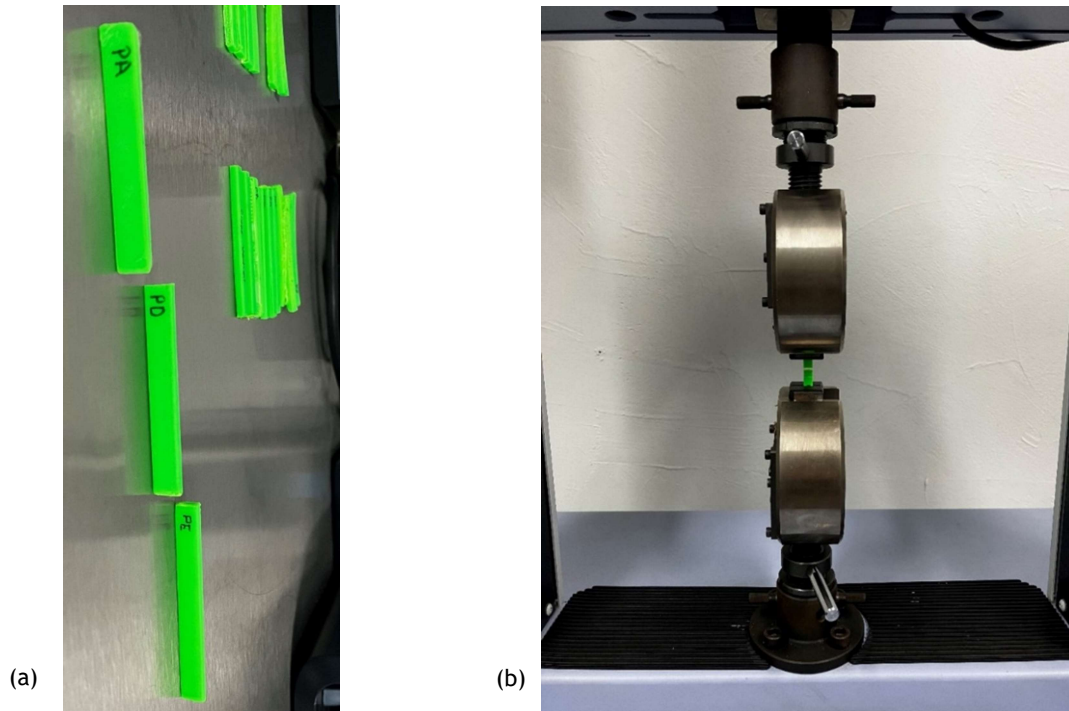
(a) Probetas impresas 3D y (b) Ensayo de tensión.
